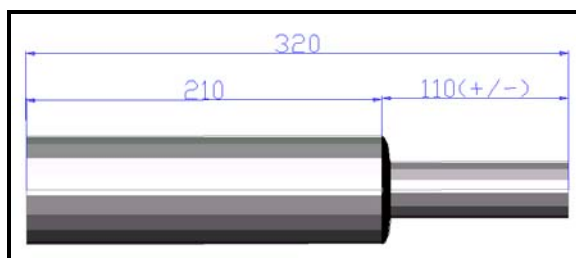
Dimensões do cilindro que deverá ser utilizado.
